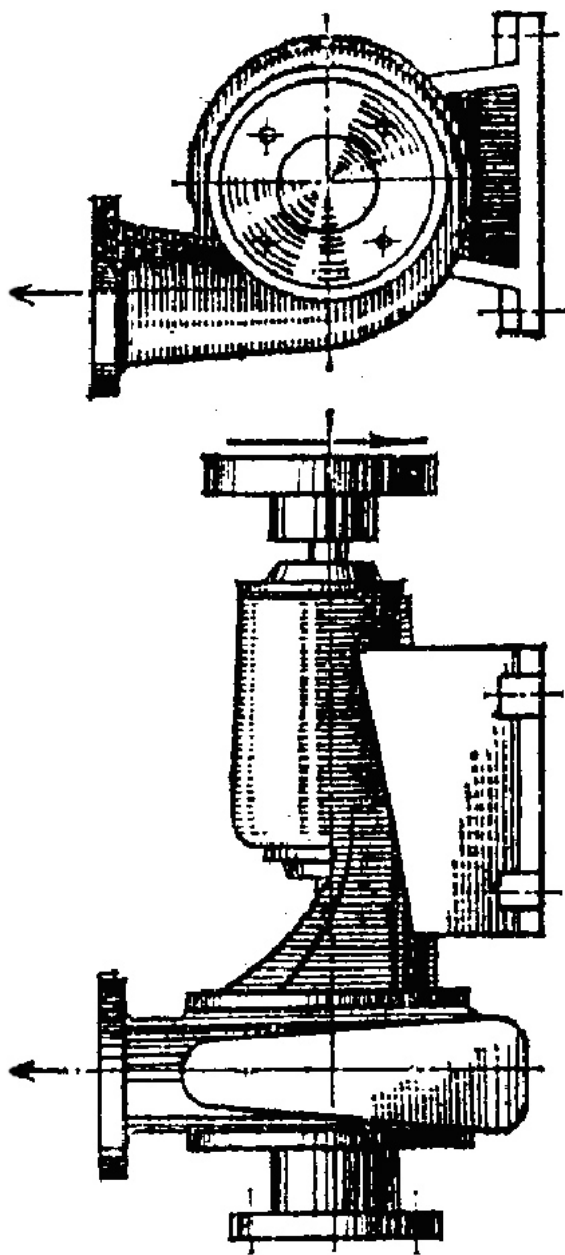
Внешний вид центробежного насоса типа К с напорным патрубком, обращенным вверх
